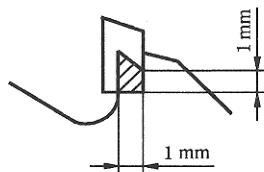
焊接圆锯片刀头的最小尺寸
